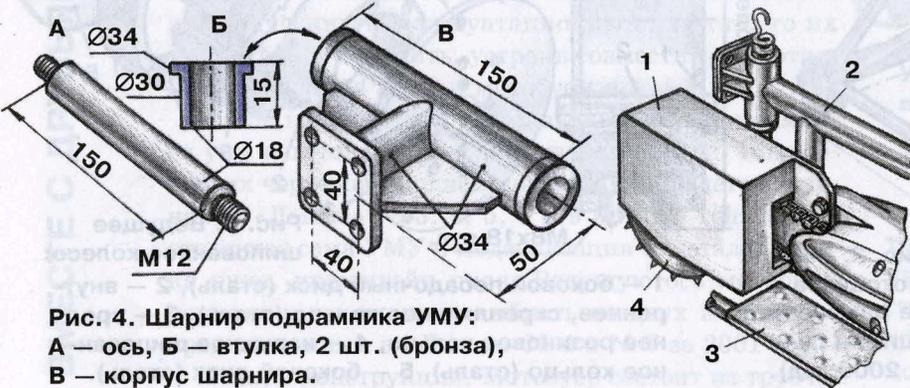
Шарнир подрамника УМУ: А — ось, Б — втулка, 2 шт. (бронза), В — корпус шарнира.
